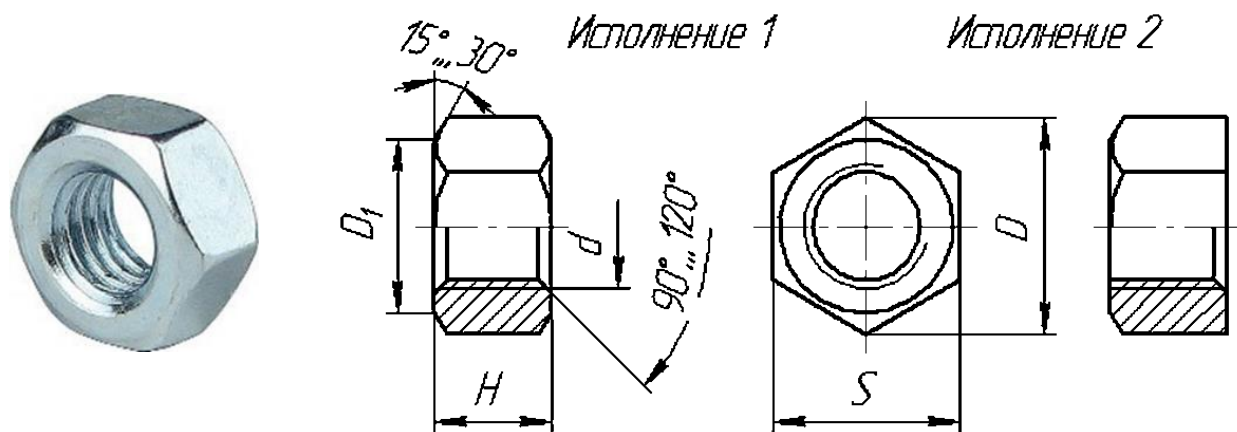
Из Образец выполнения шестигранной гайки.
